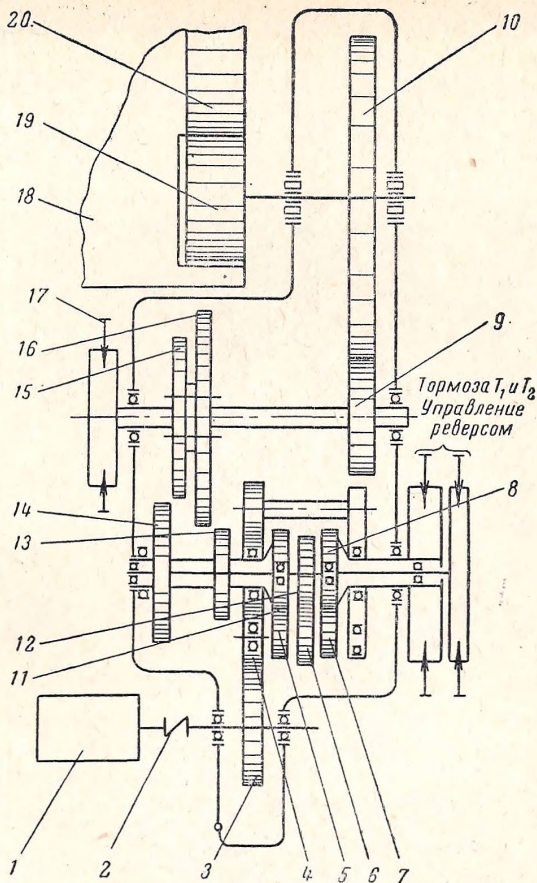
Кинематическая схема моторного катка Д-399А:
